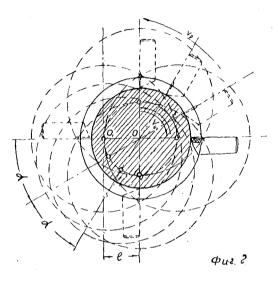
Схема охватывающего фрезерования при невращающейся детали.
